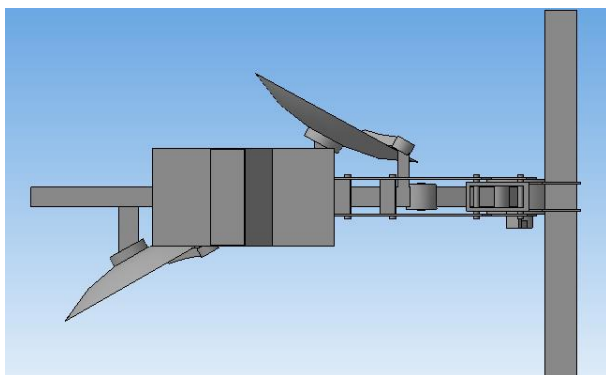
Вид сверху предлагаемой конструкции окучника
